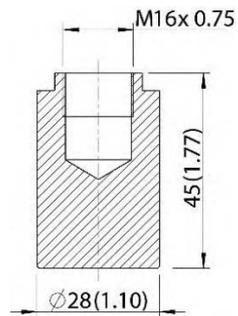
Vue et dimensions de l'outil d'extraction (E-TJET)
